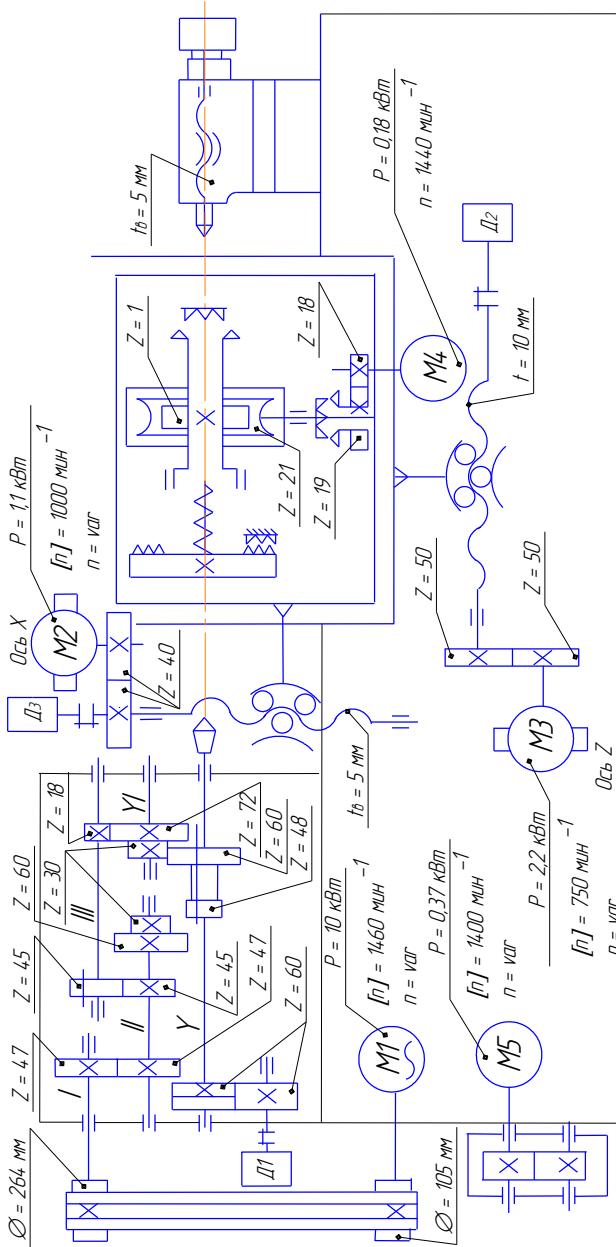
Кинематическая схема станка мод.16К20Т1
